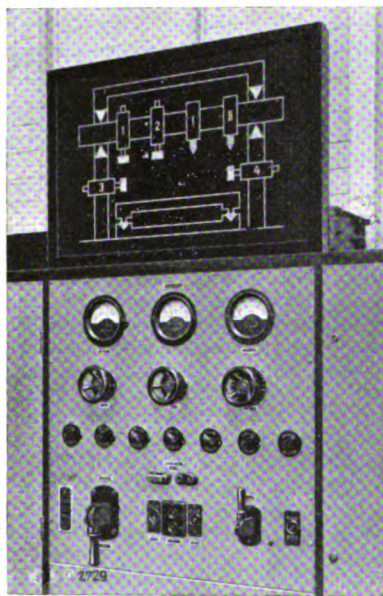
Leuchtschaltbild für eine vereinigte Hobel- und Fräsmaschine.
